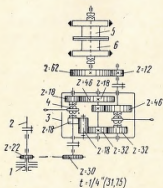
Кинематическая схема крана-трубоукладчика Т15-30
